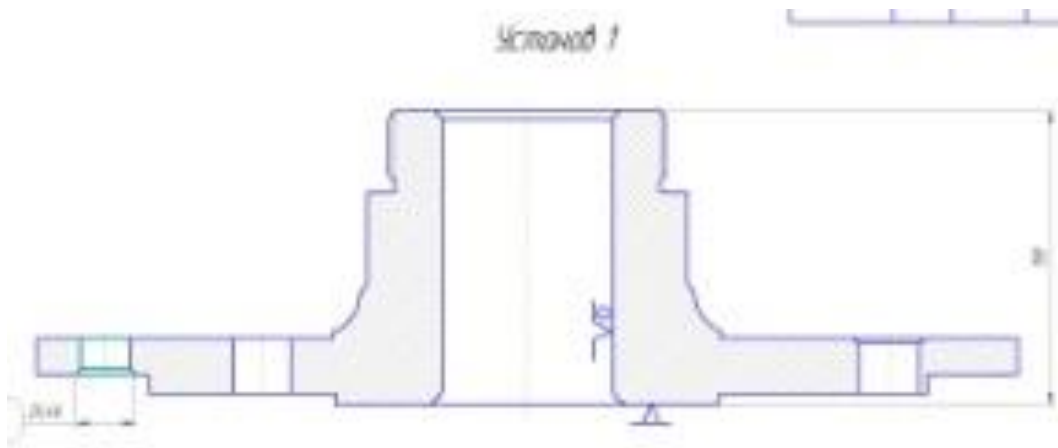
Ескіз установки деталі на свердлильній операції
